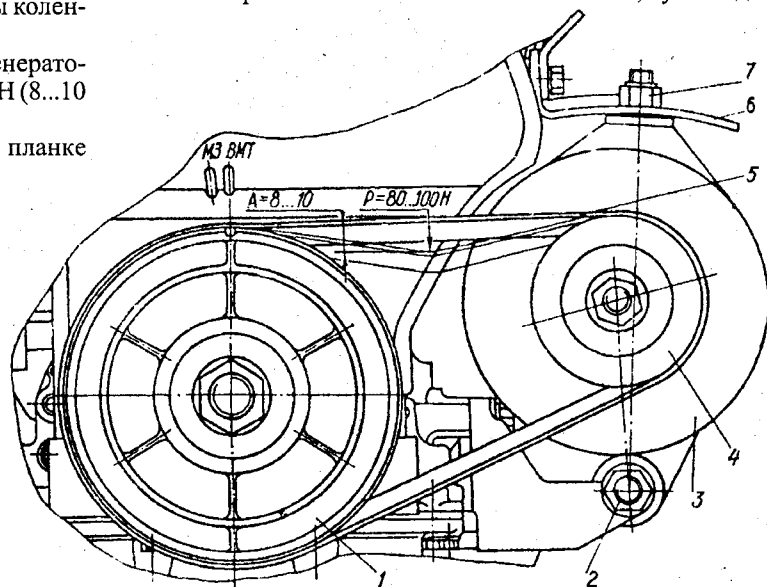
Привод генератора и проверка натяжения ремня: 1 – шкив коленчатого вала; 2 – гайка болта крепления генератора; 5 – ремень; 6 – натяжная планка; 7 – гайка крепления генератора к натяжной планке
